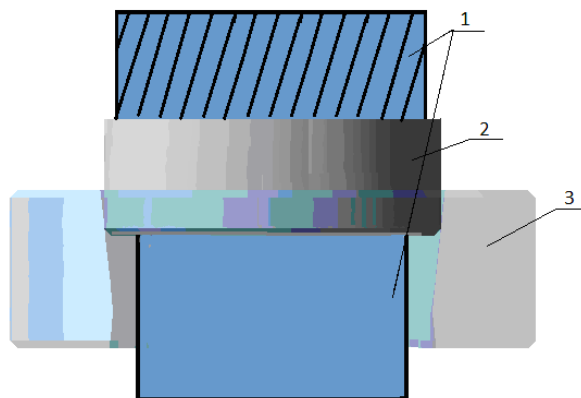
Схема процесса редуцирования: 1– ступенчатый рифленый пуансон; 2 – заготовка; 3 – матрица
